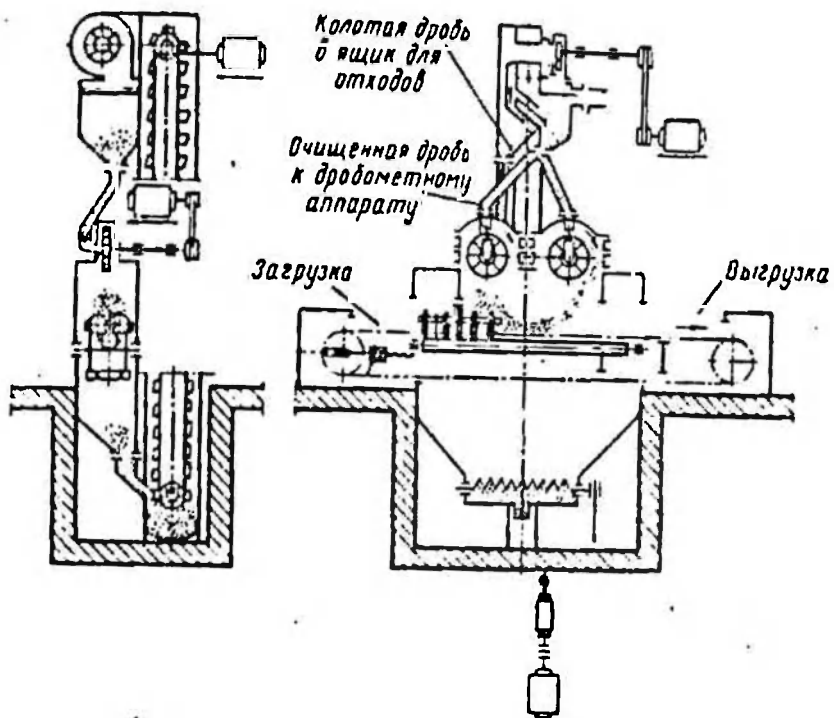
Схема установки для наклепа дробью цилиндрических зубчатых колес
